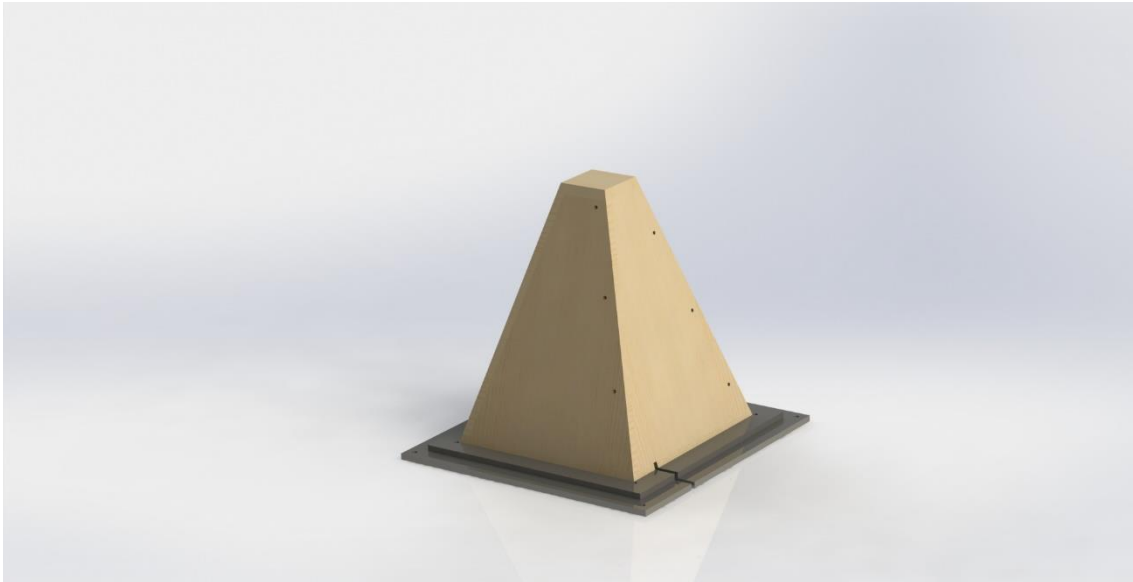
Caja de madera sobre soporte base. Fuente: elaboración propia
